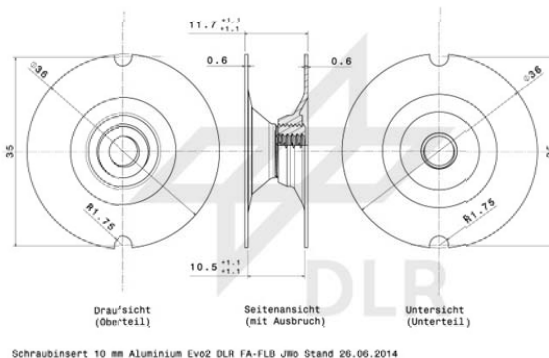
Dimensionsmaße des Insertprototyps Schraubinsert Aluminium, 10 mm (für Sandwichtyp 616 HC)
